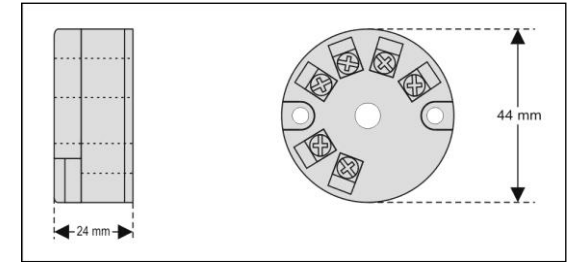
Dimensões do transmissor TxIsoPack-HART
